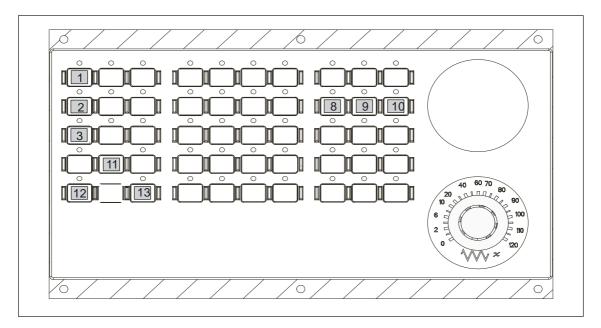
Tastenbelegung Maschinensteuertafel für OP032S
